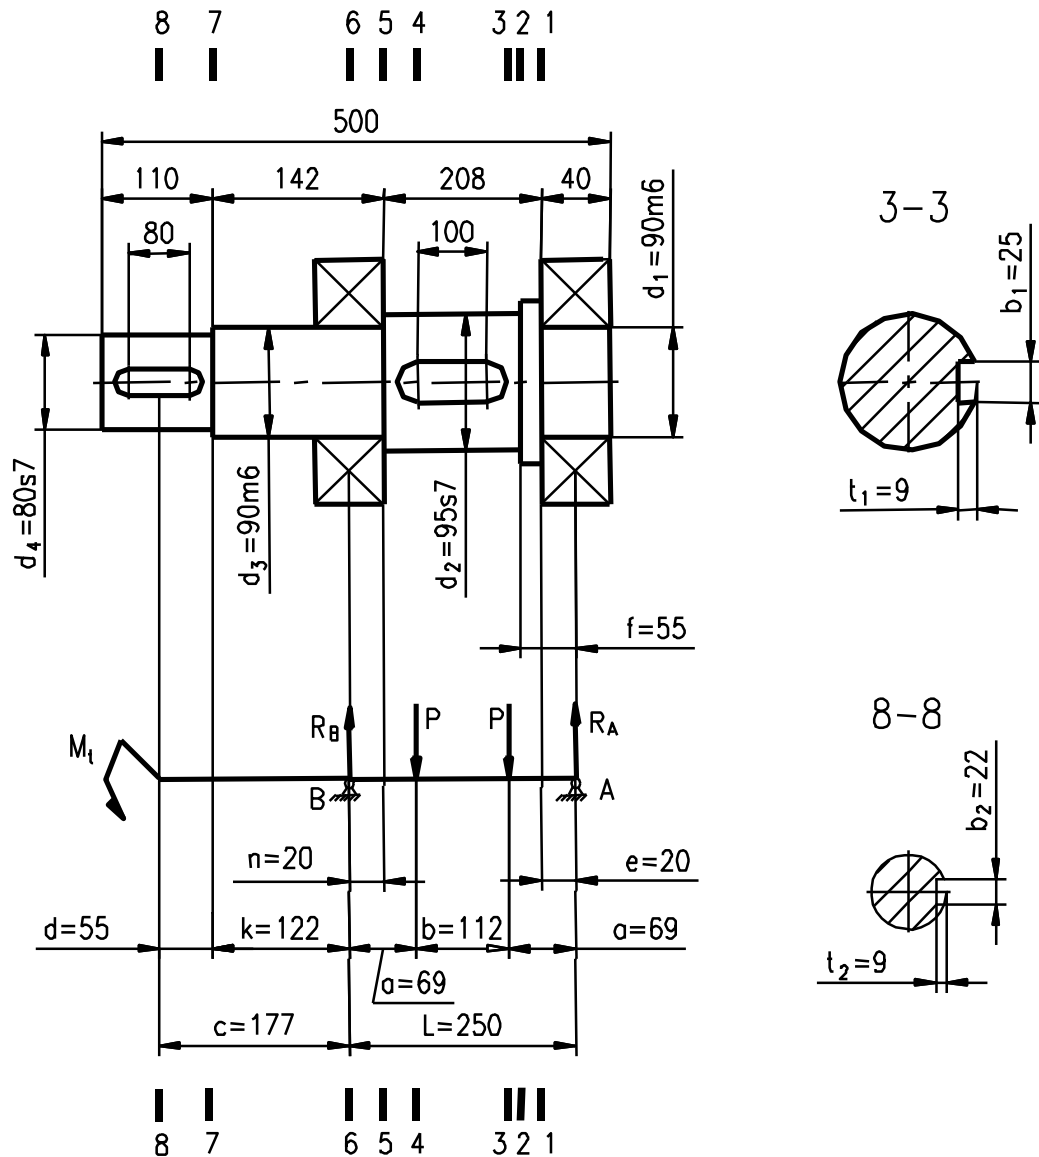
Розрахункова схема вала привідного колеса візка.
